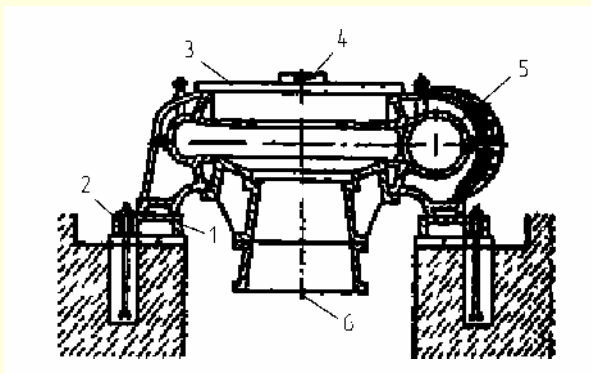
Установка и выверка корпуса насоса типа В:
